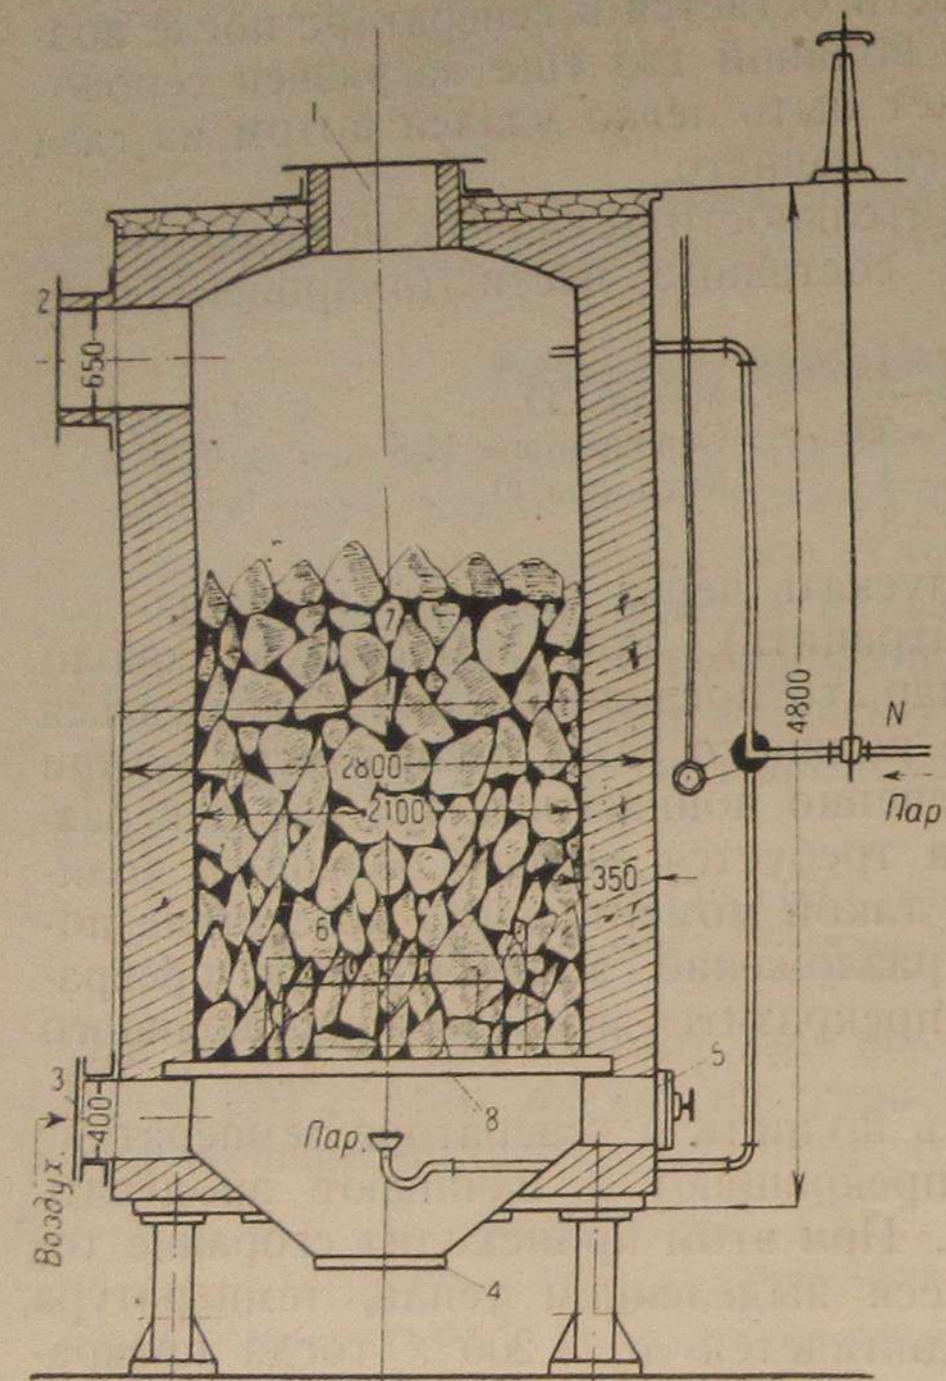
а. Генератор водяного газа системы Пинча: 1 — загрузочное отверстие; 2 — штуцер выхода газа; 3 — вход воздуха и выход газа (газование сверху); 4 — зольник; 5 — поддувало; 6 — шлаковые дверцы; 7 — шахта генератора; 8 — колосниковая решетка.
